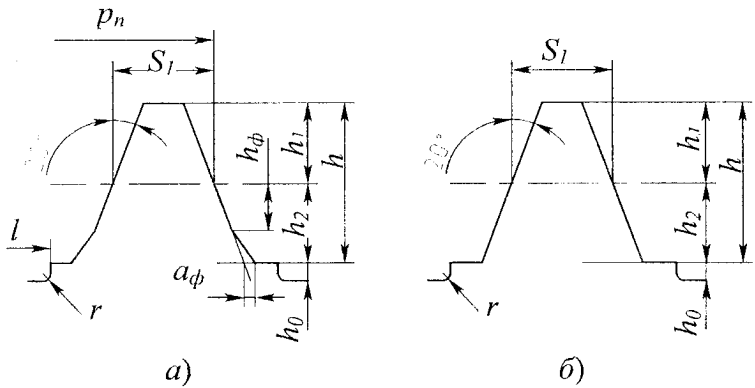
Розміри профілю зубів фрези для коліс:
